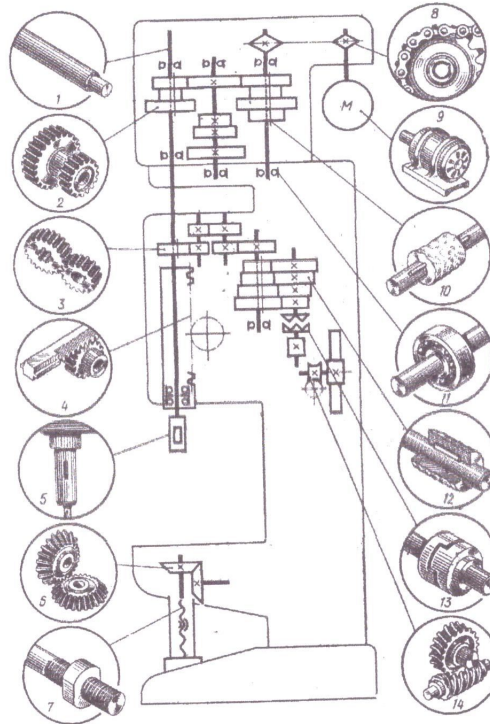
Кинематическая схема вертикально-сверлильного станка
